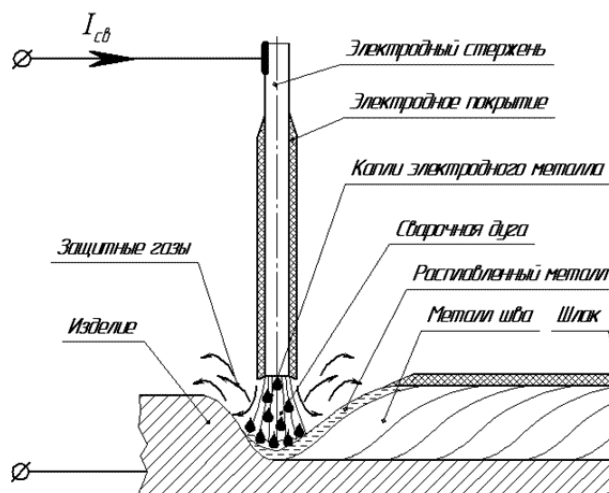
Схема процесса ручной дуговой сварки штучными электродами
